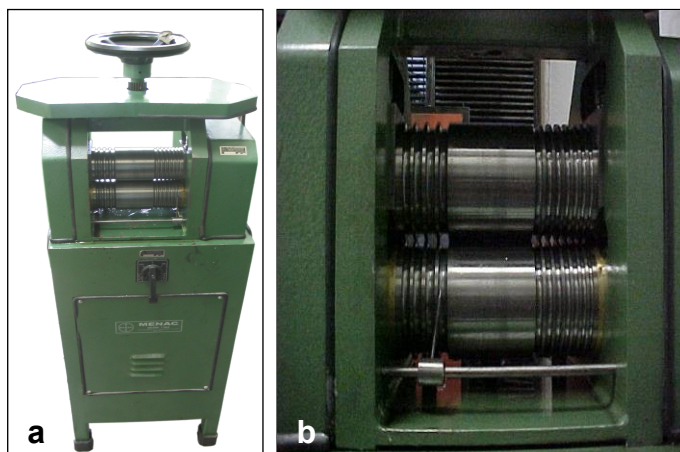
Laminador elétrico duo reversível: (a) Laminador “corpo” inteiro; (b) detalhe do canal de laminação.
